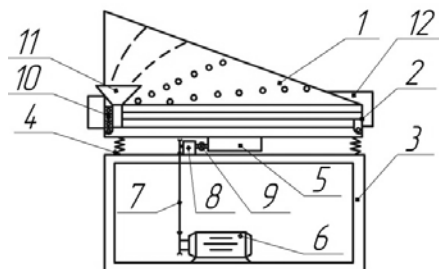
Конструктивна схема віброфрикційного сепаратора: 1 – робочі поверхні; 2 – пакет робочих поверхонь; 3 – рама; 4 – пружна підвіска; 5 – віброзбудник; 6 – електродвигун; 7 – клинопасова передача; 8 – проміжна передача; 9 – муфта; 10 – механізм встановлення кута нахилу пакету робочих поверхонь; 11 – завантажувальне пристосування; 12 – приймальники продуктів розділення
